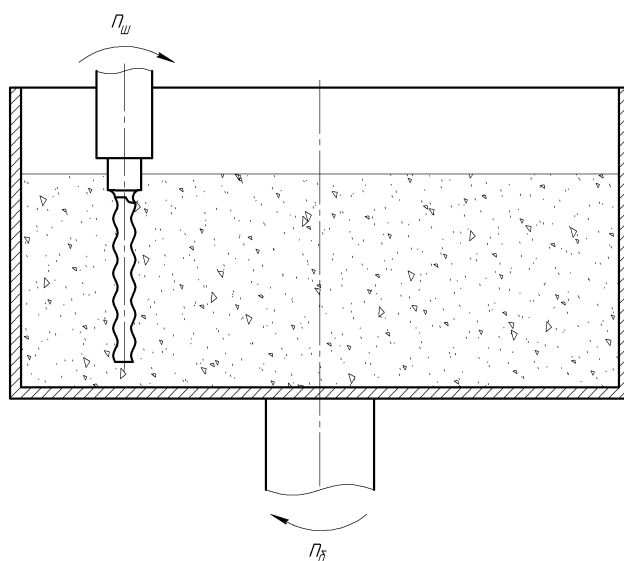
Схема обработки заготовок методом потоковой галтовки
